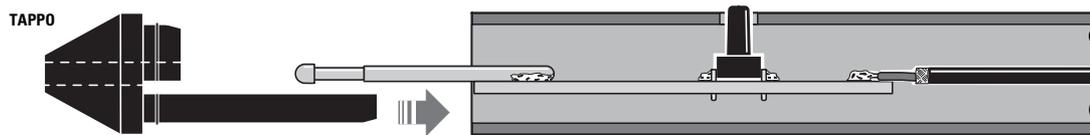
extraed la tapa e insertadla dentro del tubo, para que la guía de plástico se encuentre debajo del impreso como indica la flecha del dibujo.
